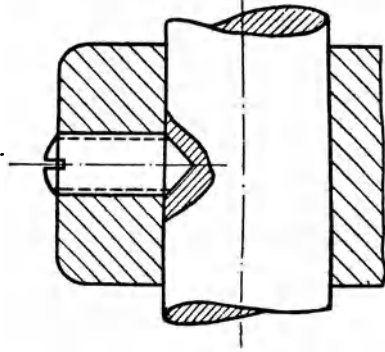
Rinnenbildung des Gewindekopfes mit Spitze.
